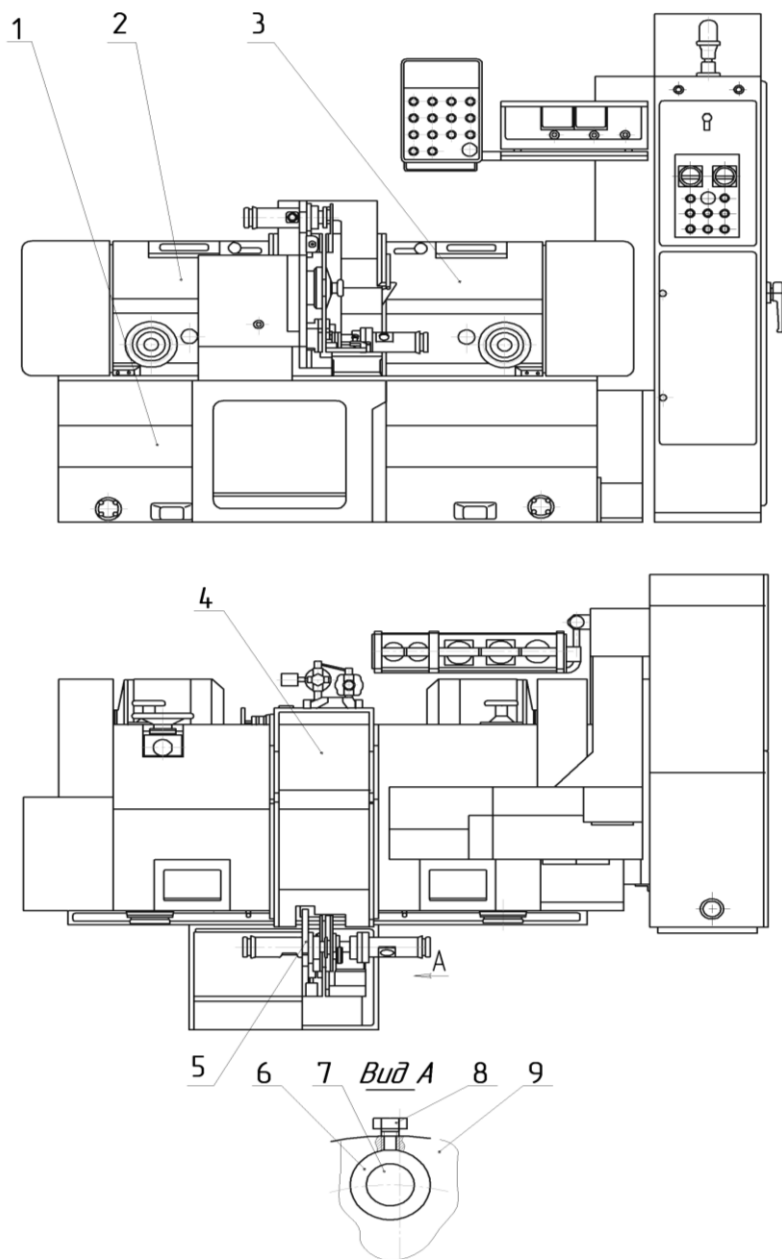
Общий вид двустороннего торцешлифовального станка 3342 АДО
